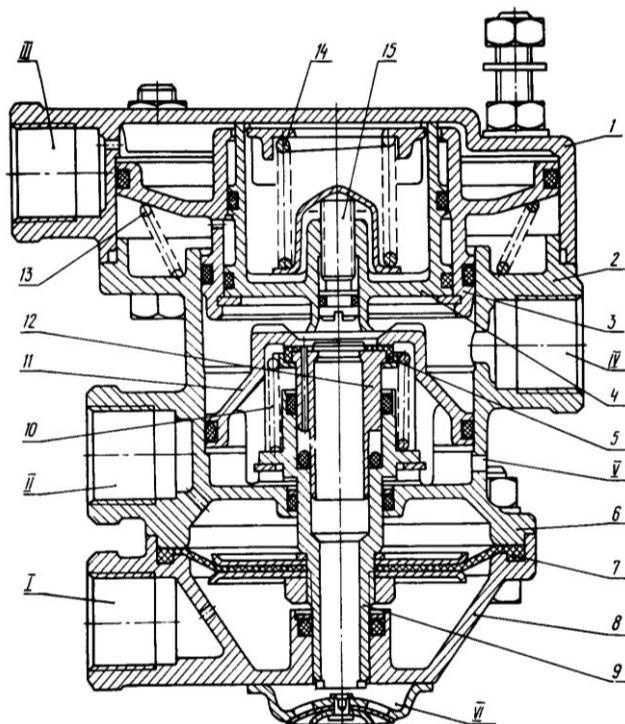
Клапан управления тормозами полуприцепа с двухпроводным приводом: 1 – крышка верхняя; 2 – корпус; 3 – поршень верхний; 4, 9 – поршни; 5 – клапан; 6 – корпус; 7 – диафрагма; 8 – крышка нижняя; 10, 13, 14 – пружины; 11 – поршень средний; 12 – корпус; 15 – винт
